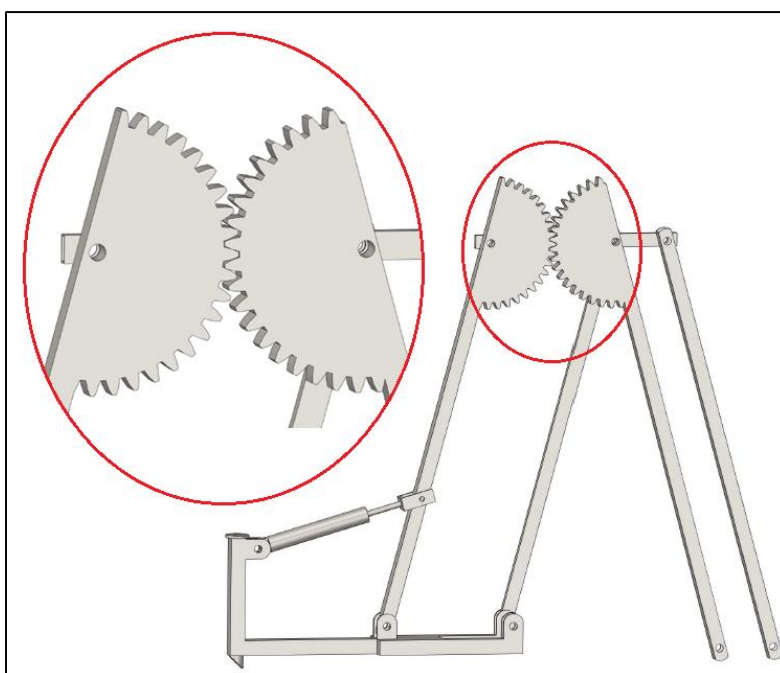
Disposición del engranaje en el mecanismo
